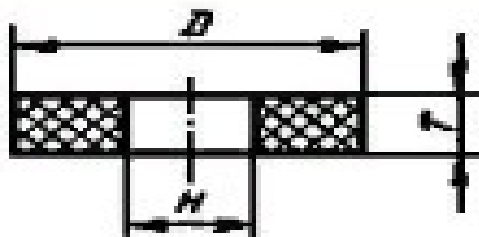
Круг шлифовальный 25x40x20 24А 10-П 7 КППГ 35м/с
